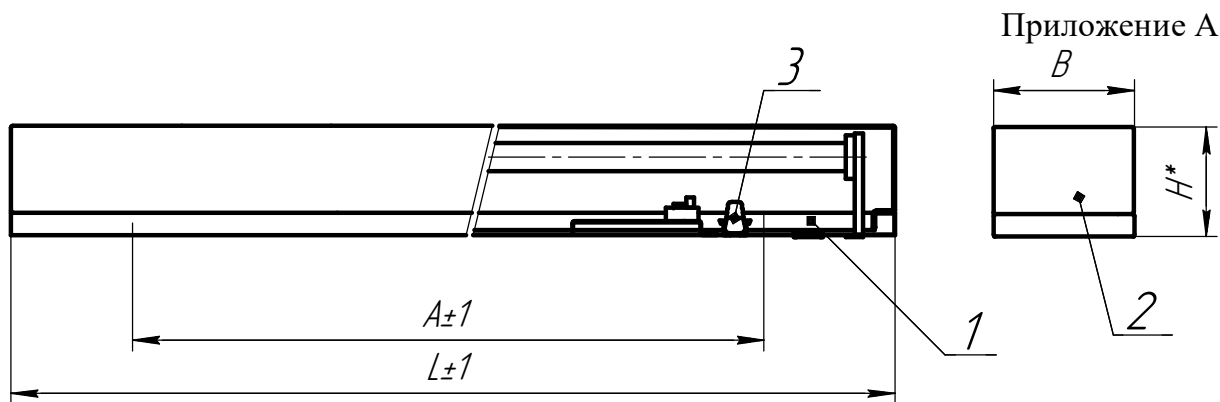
ЛПО46-18; 36; 2x18; 2x36 1. корпус в сборе; 2. рассеиватель; 3. защелка
